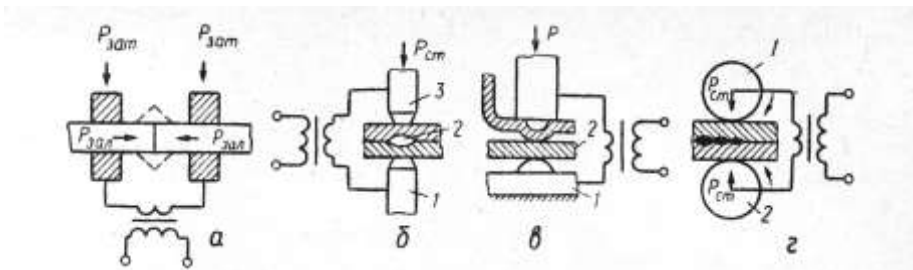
Схема контактного зварювання: а – стикового; б – точкового; в – рельфного; г – шовного
